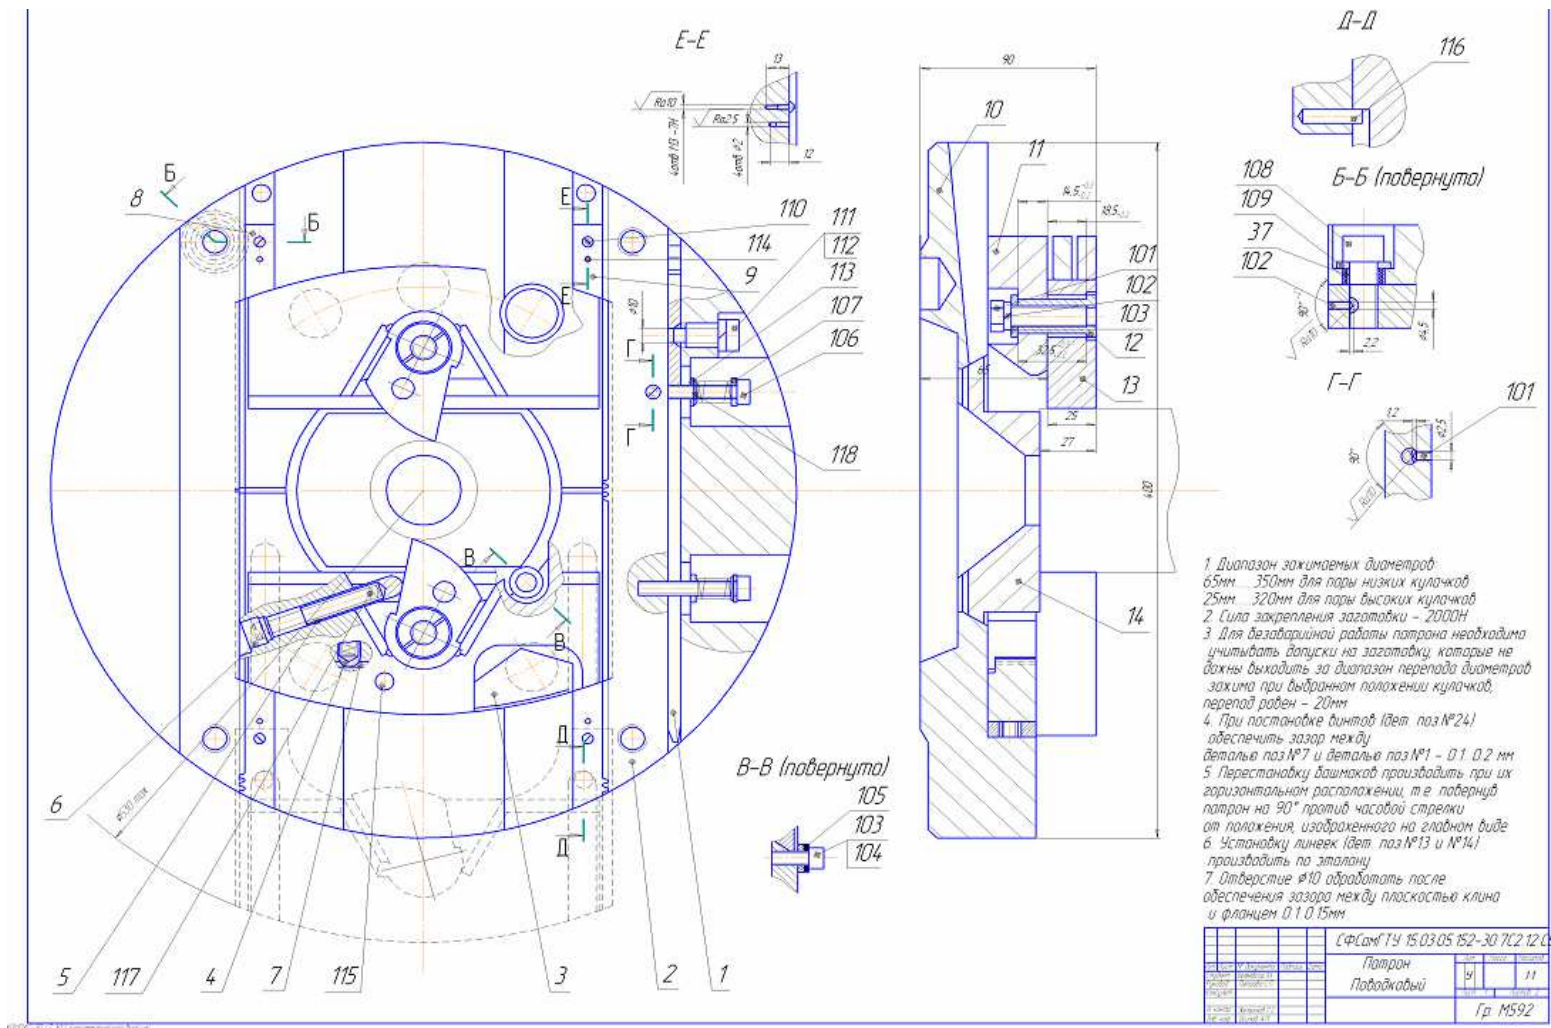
Пример выполнения чертежа станочного приспособления
